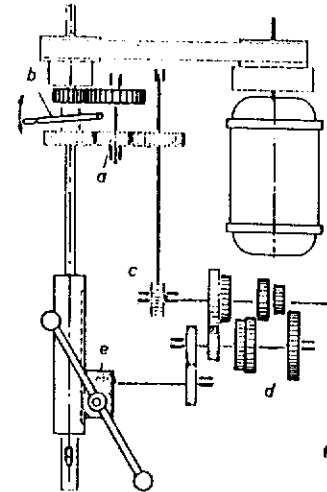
,1. Movimiento principal y de avance en una máquina de taladrar. a) Engranajes para el movimiento principal; b) palanca de embrague para el movimiento principal; c) derivación para el movimiento de avance por medio de rueda helicoidal y tornillo sin fin; d) sistema de engranajes desplazables para variar el avance; e) rueda helicoidal y tornillo sin fin para producir el avance.
